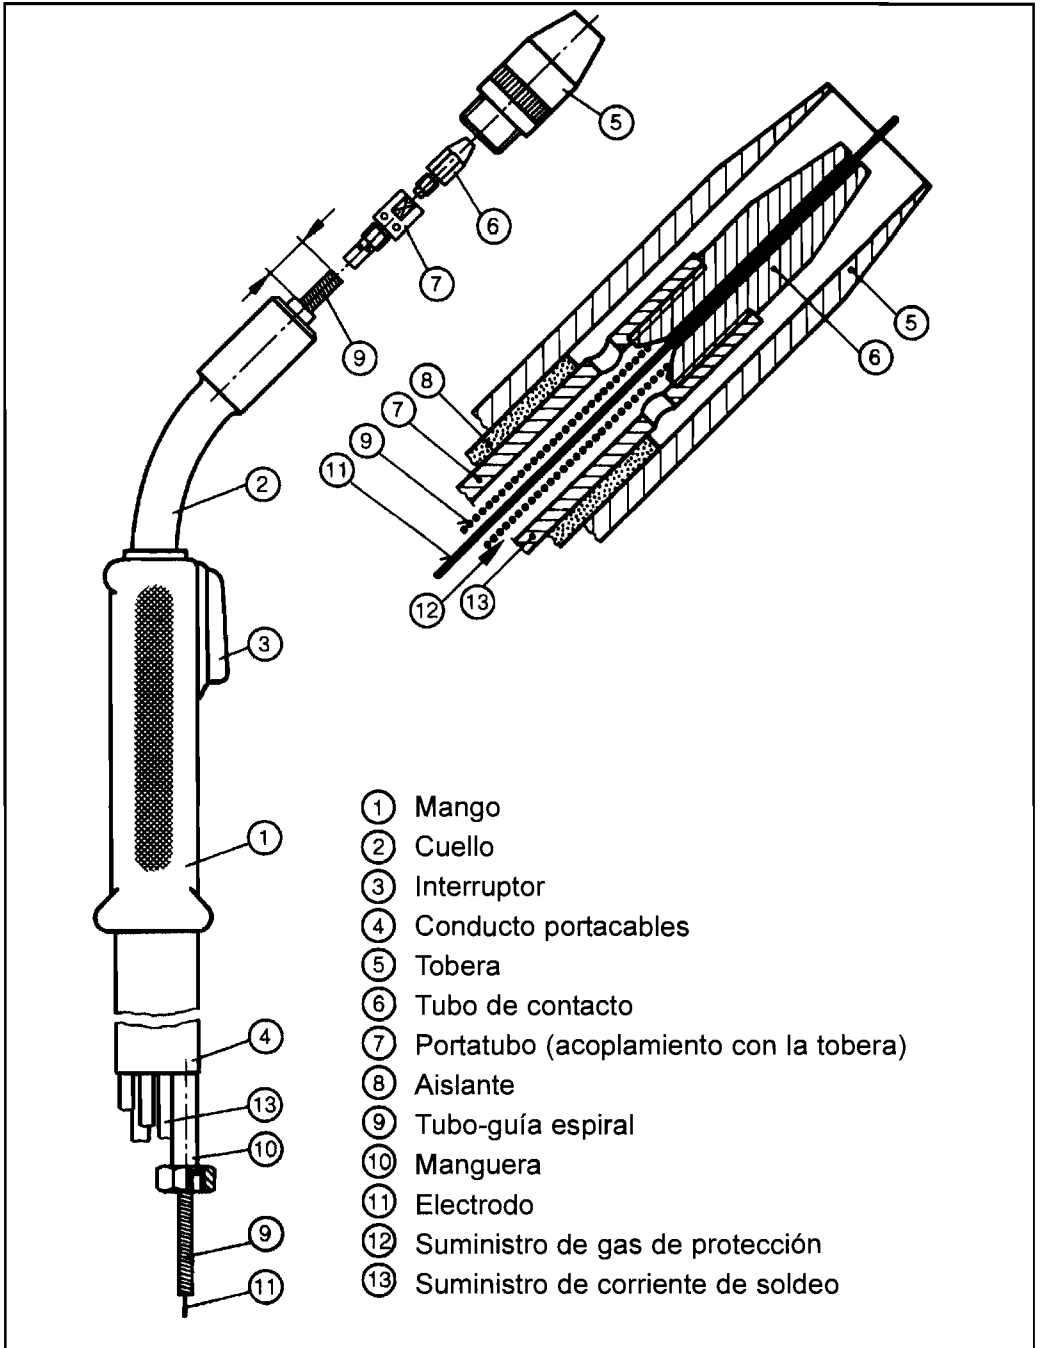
PISTOLA PARA SOLDEO MIG/MAG (ACERO AL CARBONO)
